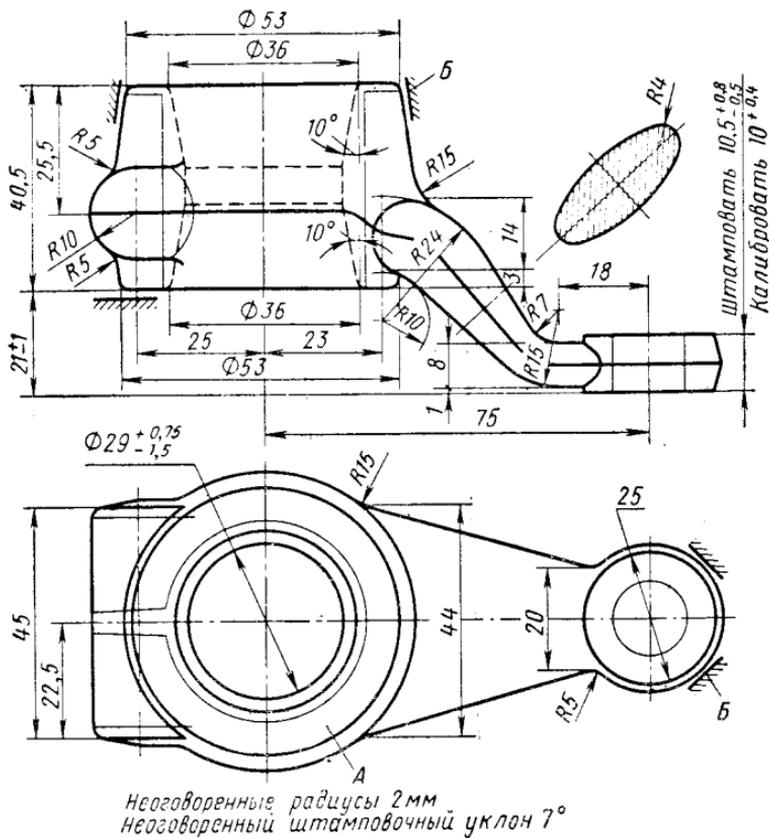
Чертеж поковки рычага переключателя из стали 45 массой 0,9 кг:
